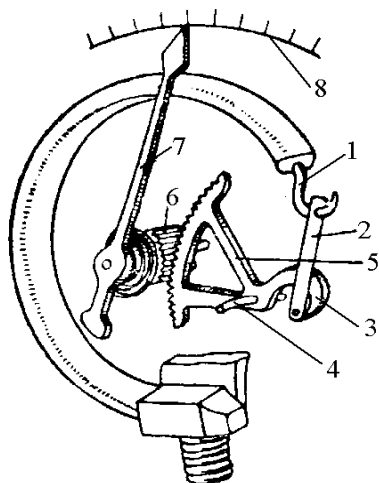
Конструктивний вигляд трубчатого механічного манометра.
